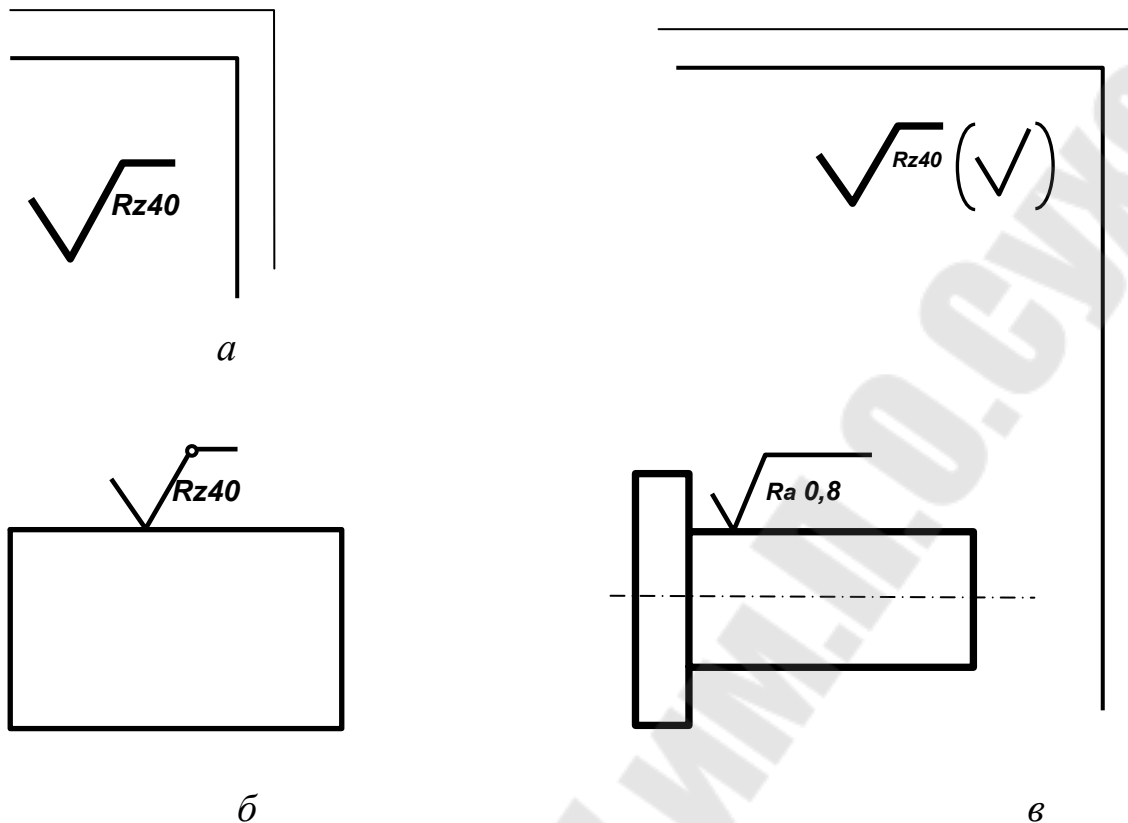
Примеры обозначения шероховатости поверхности на чертежах деталей: а – расположение знака шероховатости регламентирующего шероховатость всех поверхностей детали конкретного чертежа; б – указание шероховатости одинаковой для всех поверхностей детали образующих замкнутый контур; в – пример указания шероховатости поверхности, отличающейся от шероховатости остальных поверхностей детали.
